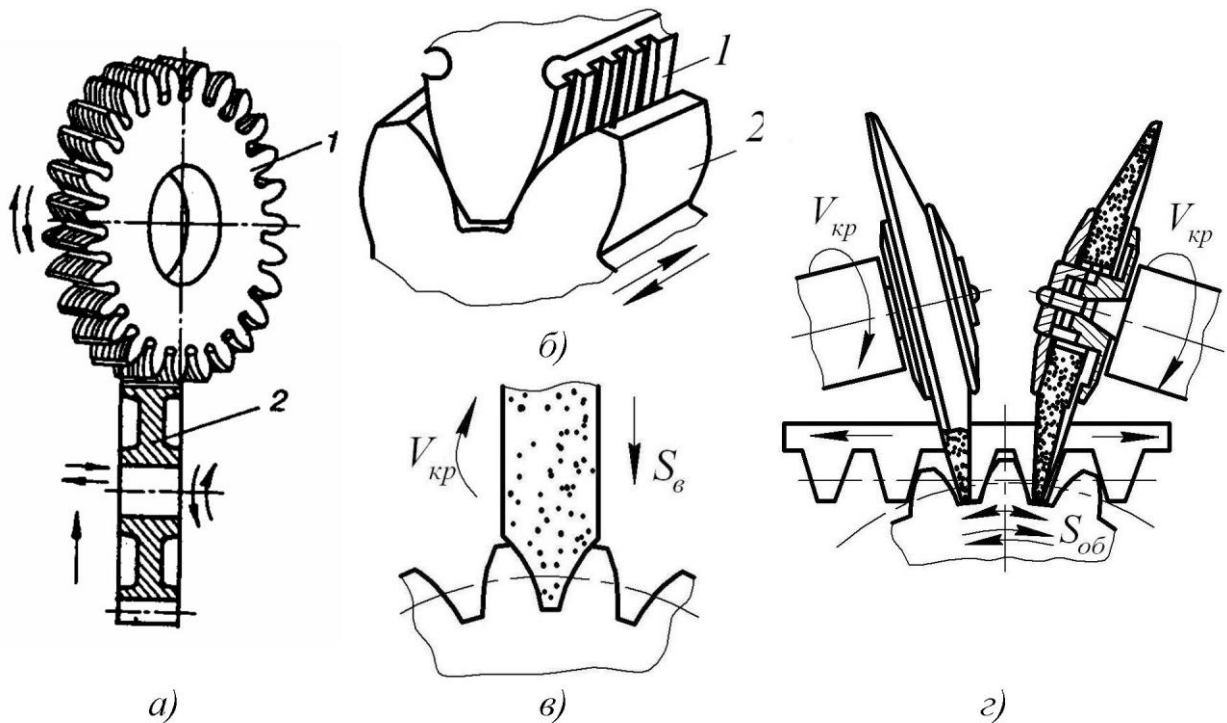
Схеми чистової обробки зубів зубчастих коліс
